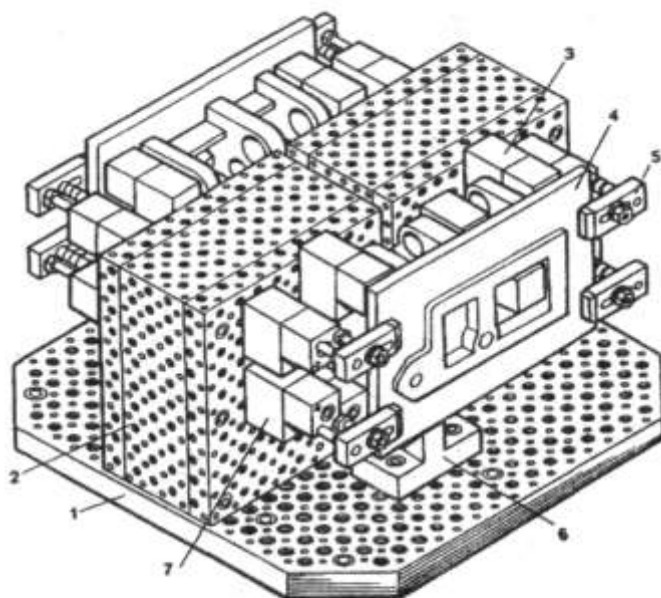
Двухместное гидравлическое приспособление для установки корпусной детали
